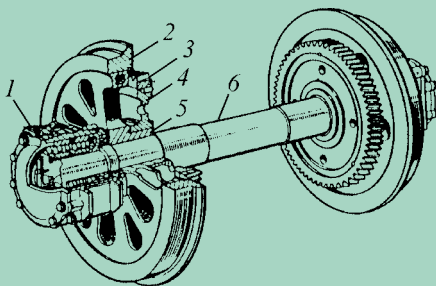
Колесная пара электровоза: 1 — букса; 2 — бандаж; 3 — венец зубчатого колеса; 4 — центр зубчатого колеса; 5 — колесный центр; 6 — ось
